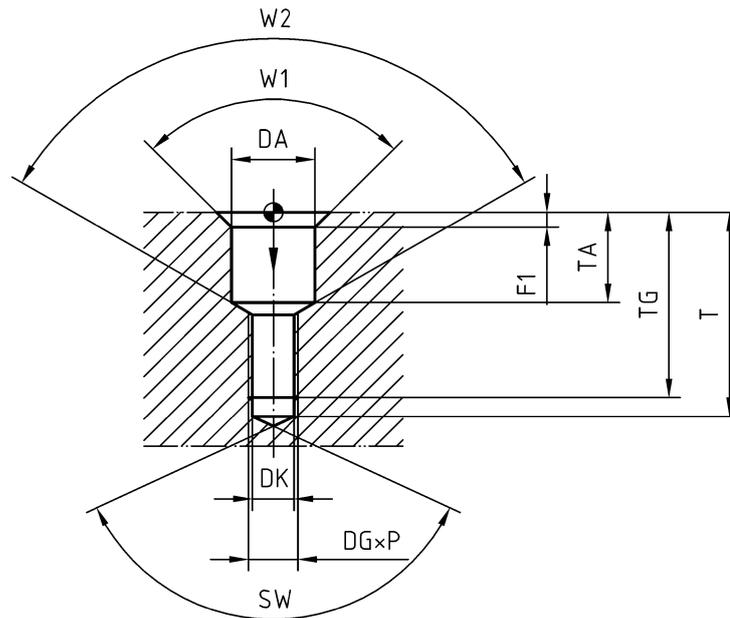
Gewindegrundbohrung mit Aufbohrung
